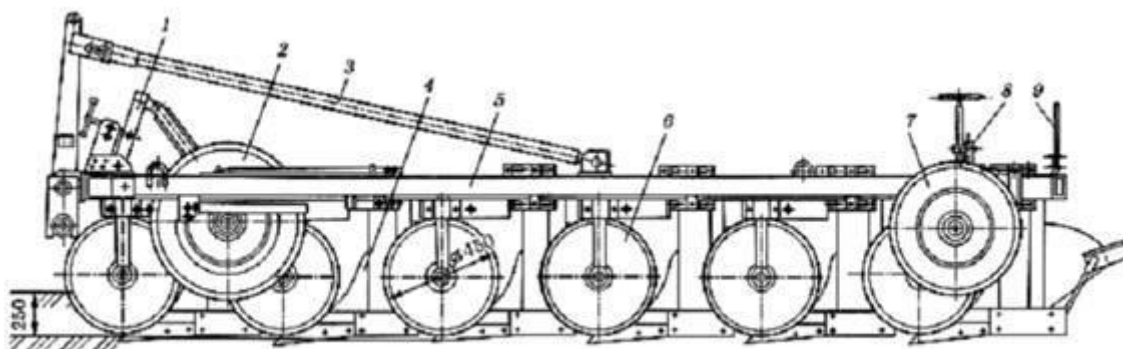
Конструктивна схема чагарниково-болотного плуга ПБН-6-50:
